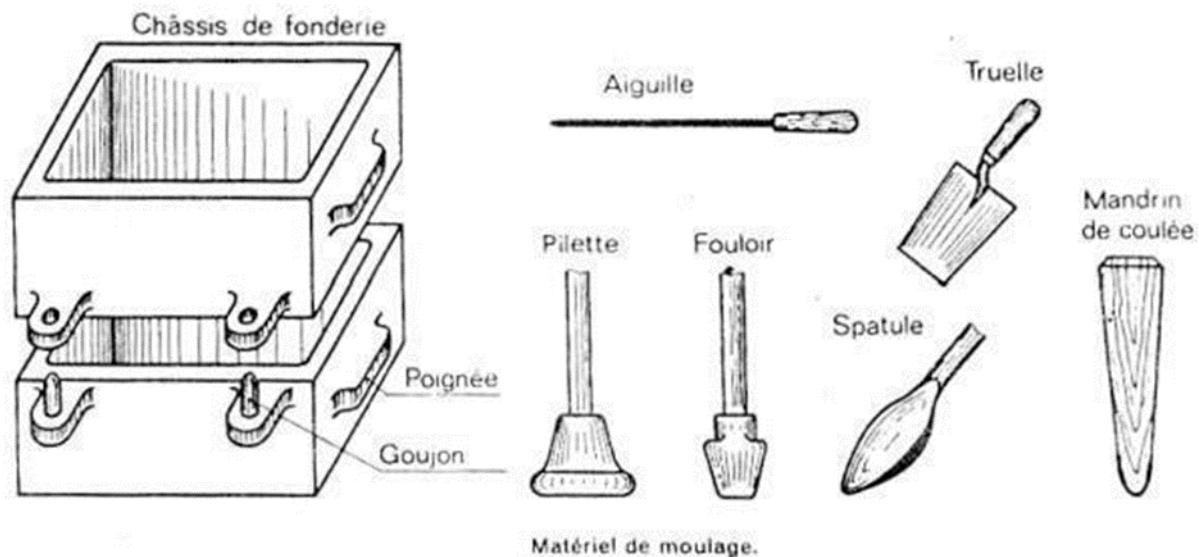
Matériel nécessaire pour le moulage en sable.
